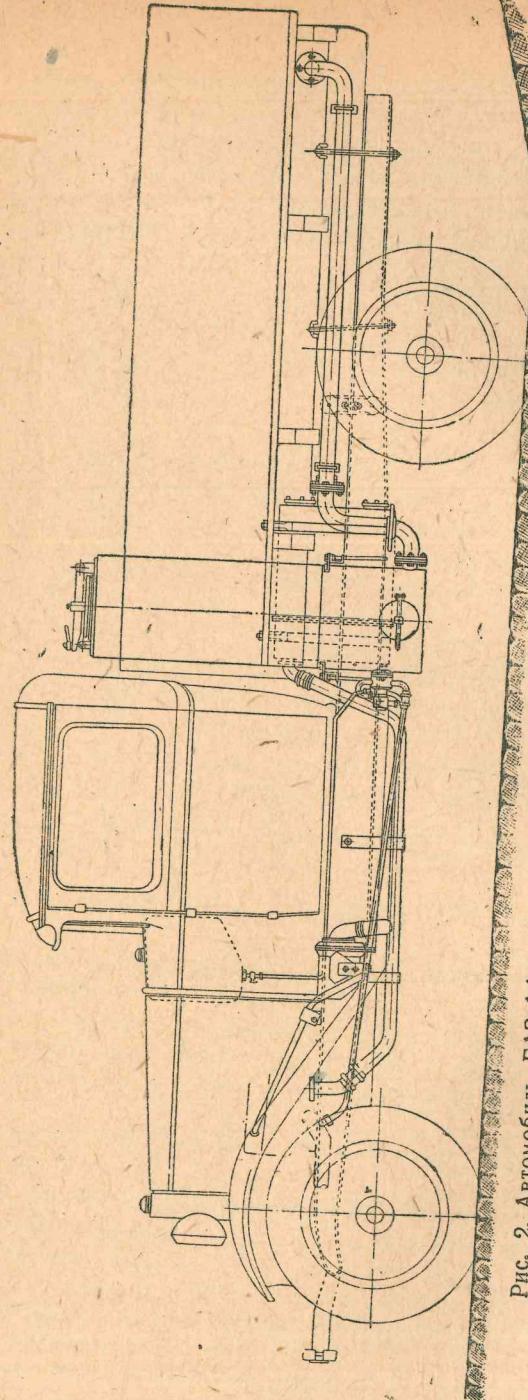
Автомобиль ГАЗ-АА, оборудованный древесноугольной установкой ЦНИИАТ-УГ-1, Вид сбоку.
